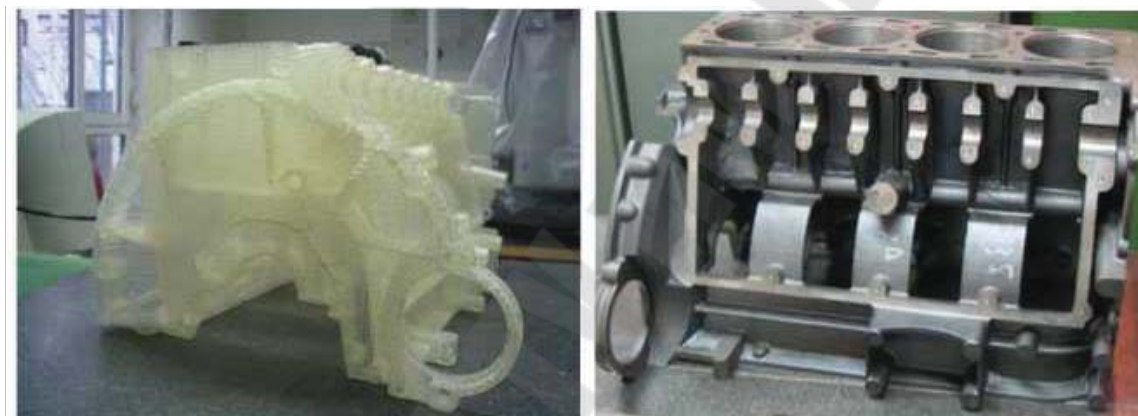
Модель и отливка блока цилиндров из чугуна
